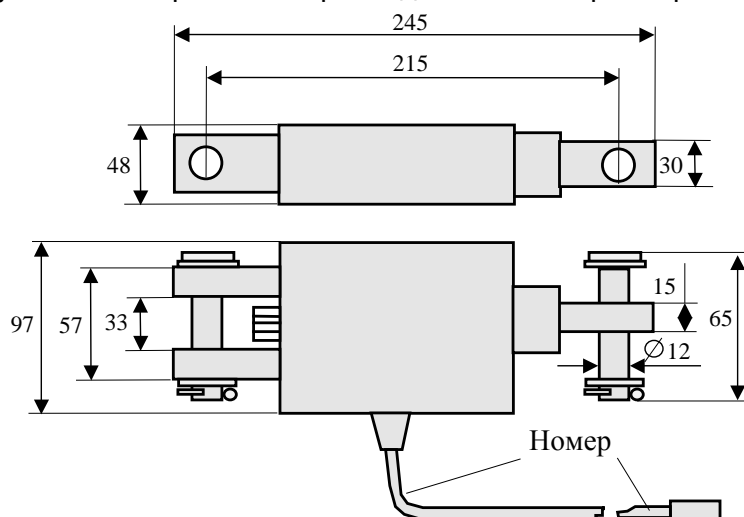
Габаритные и присоединительные размеры ПрУ
